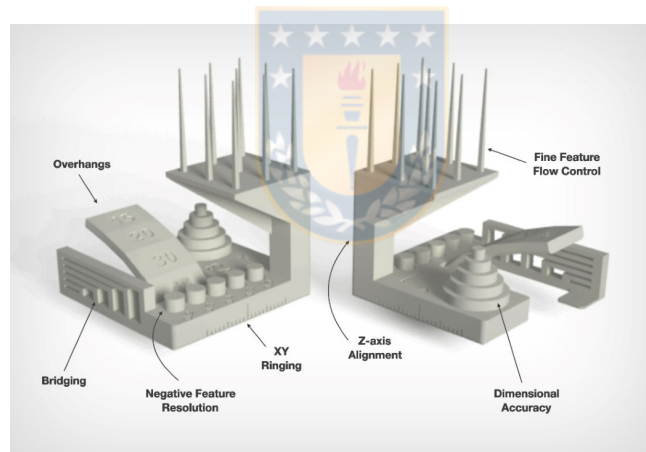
Diseño de pieza para obtener pautas geométricas de la manufactura aditiva. Imagen obtenida de [All3DP, 2020].
